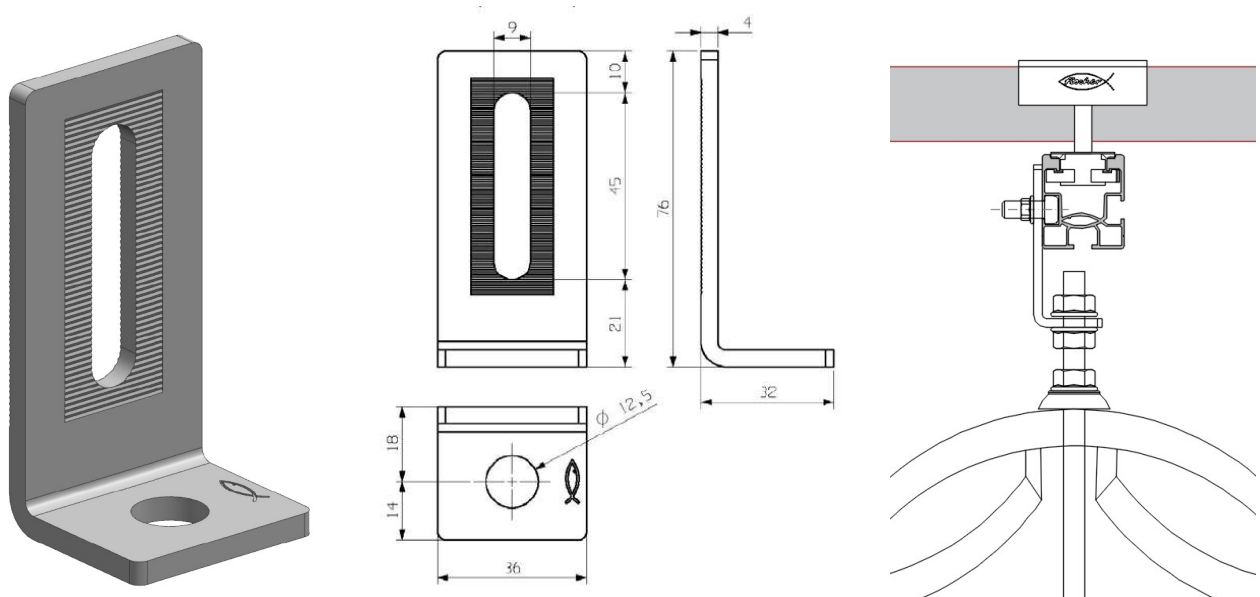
Geometria, dimensions i disposició del perfil en L MW-SA.
